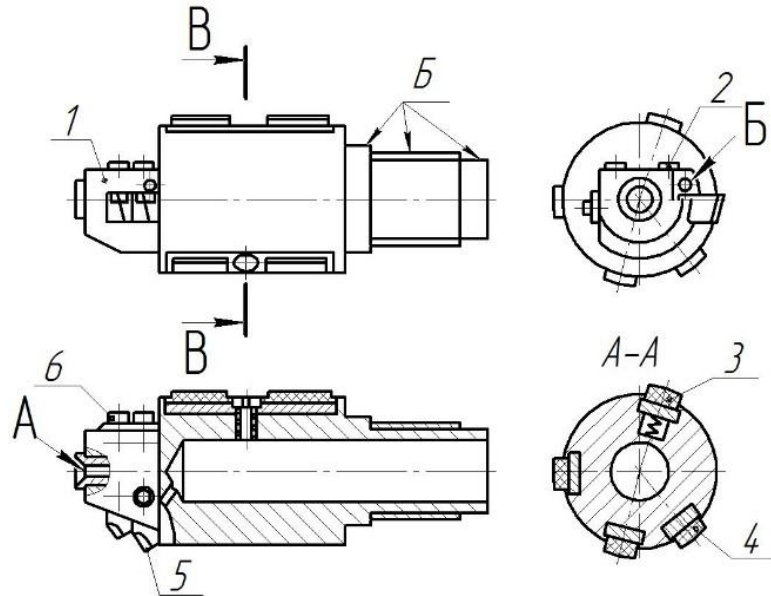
Дворізцева розточна головка з конкретним базуванням
